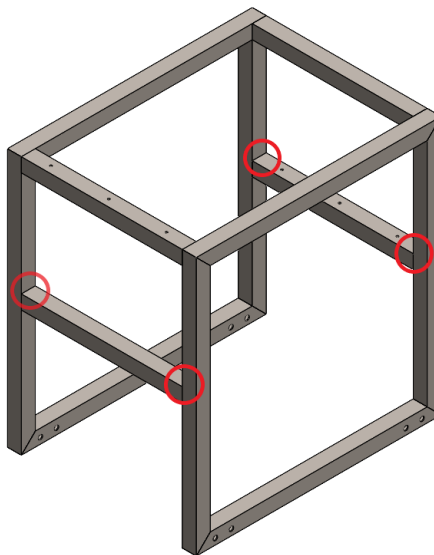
Uniones soldadas de la estructura sujetas a flexión.
